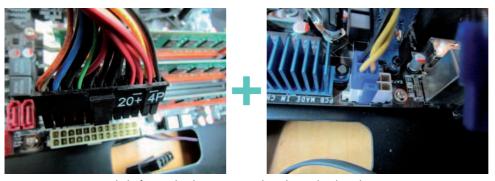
Conectores de la fuente de alimentación colocados en la placa base.
